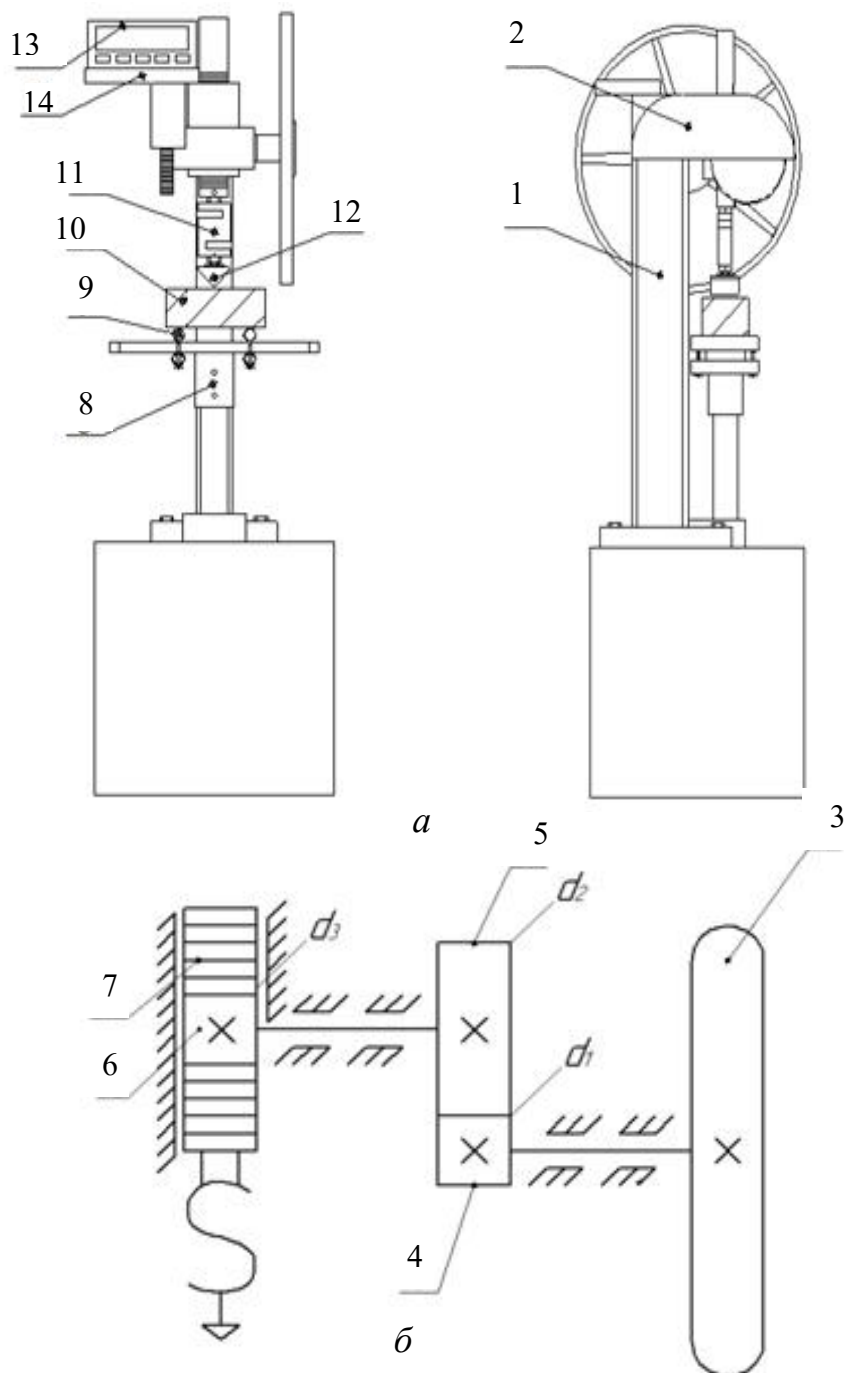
Устройство (а) и кинематическая схема стенда (б) для реализации разрушающей нагрузки и контроля изгибной прочности формованной торфяной продукции
